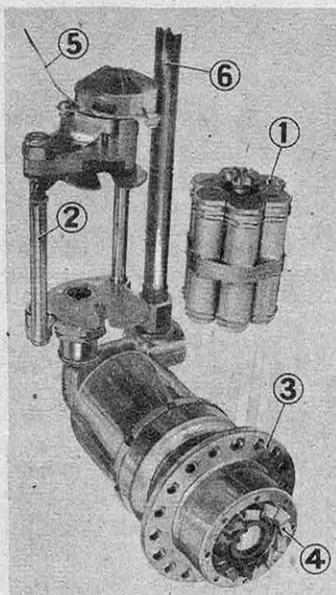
LE DÉMARREUR A EXPLOSION POUR MOTEUR DE BATEAU
